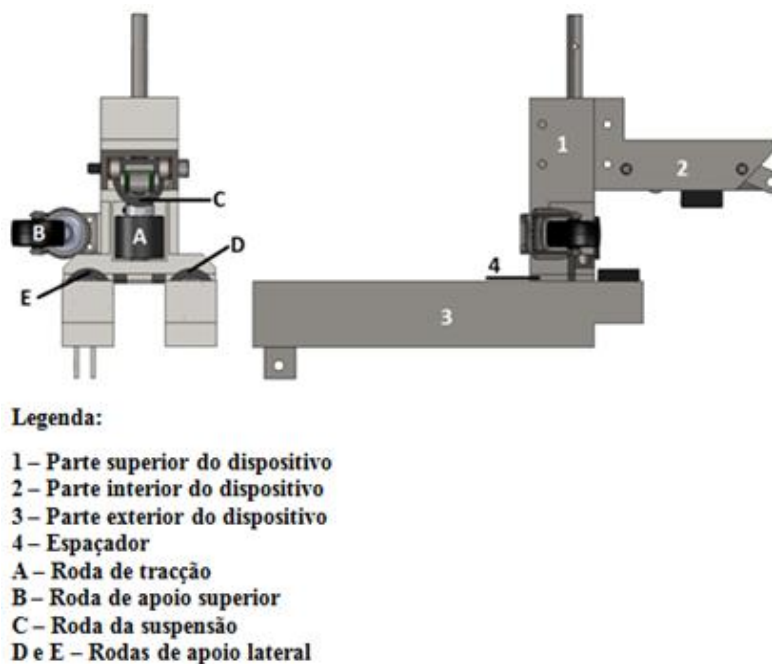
Montagem do chassis do dispositivo com as rodas colocadas
